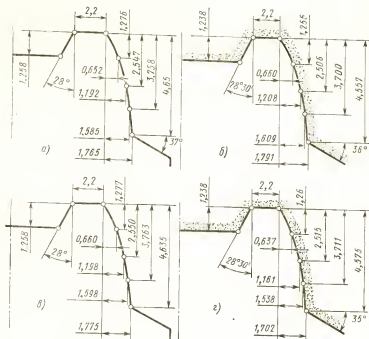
Проекция режущей кромки на плоскость контроля и профиль шлифовального круга фрез для обработки шлицевых валиков: а и б—для фрез с винтовыми канавками; в и г—для фрез с прямыми канавками
